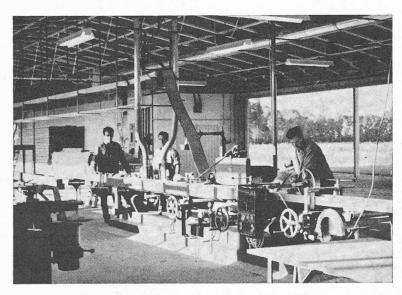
Machine spéciale Wellsteg équipant l'usine de Domdidier.
